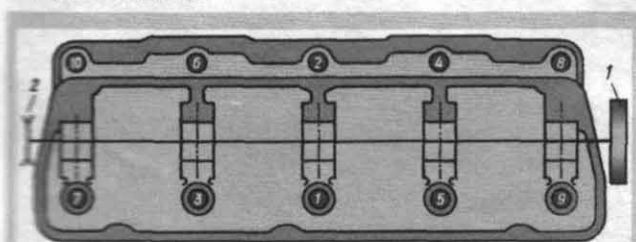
Порядок затяжки болтов крепления головки блока цилиндров: 1 – маховик; 2 – ведомый шкив коленчатого вала
